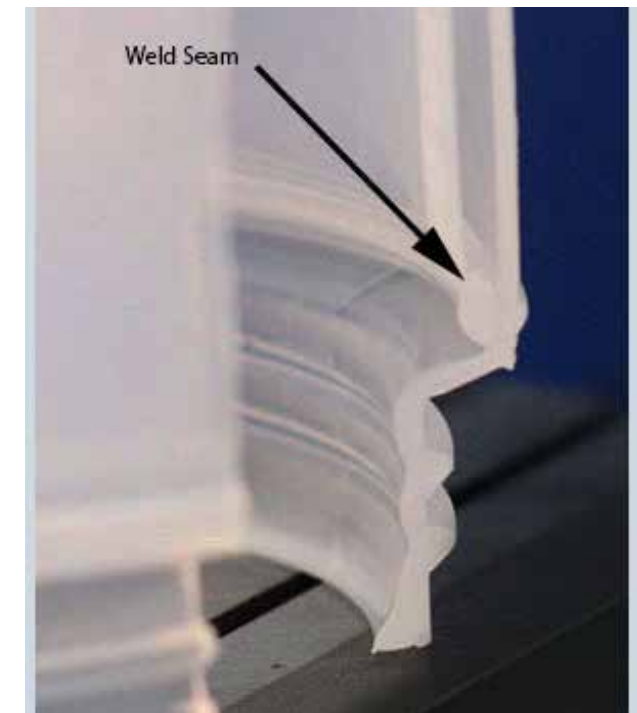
Пример части детали, полученной с помощью лазерной сварки полимеров
